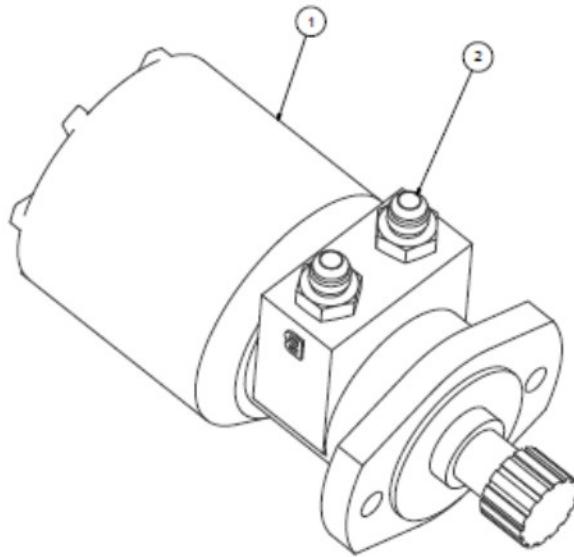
Чертеж сборки двигателя толкателя – 815679
